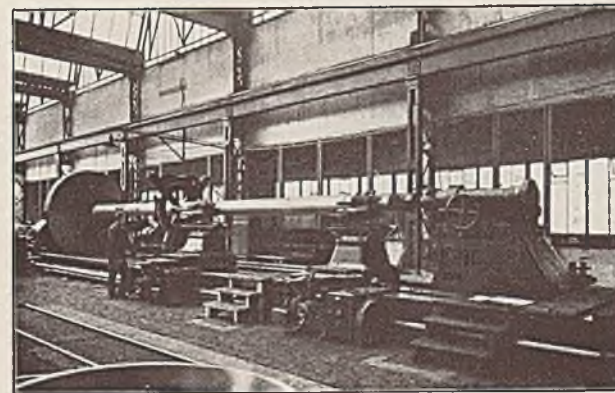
Schraubenwelle auf der Schruppbank, ca. 10000 mm lang
